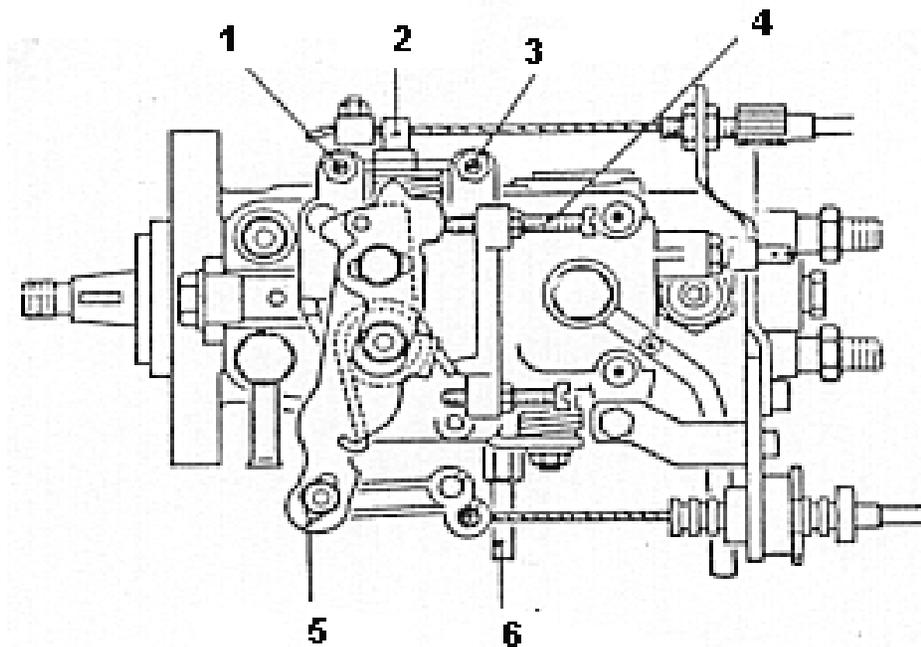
Elementos de reglaje de Reglaje de Bomba Mecánica.
